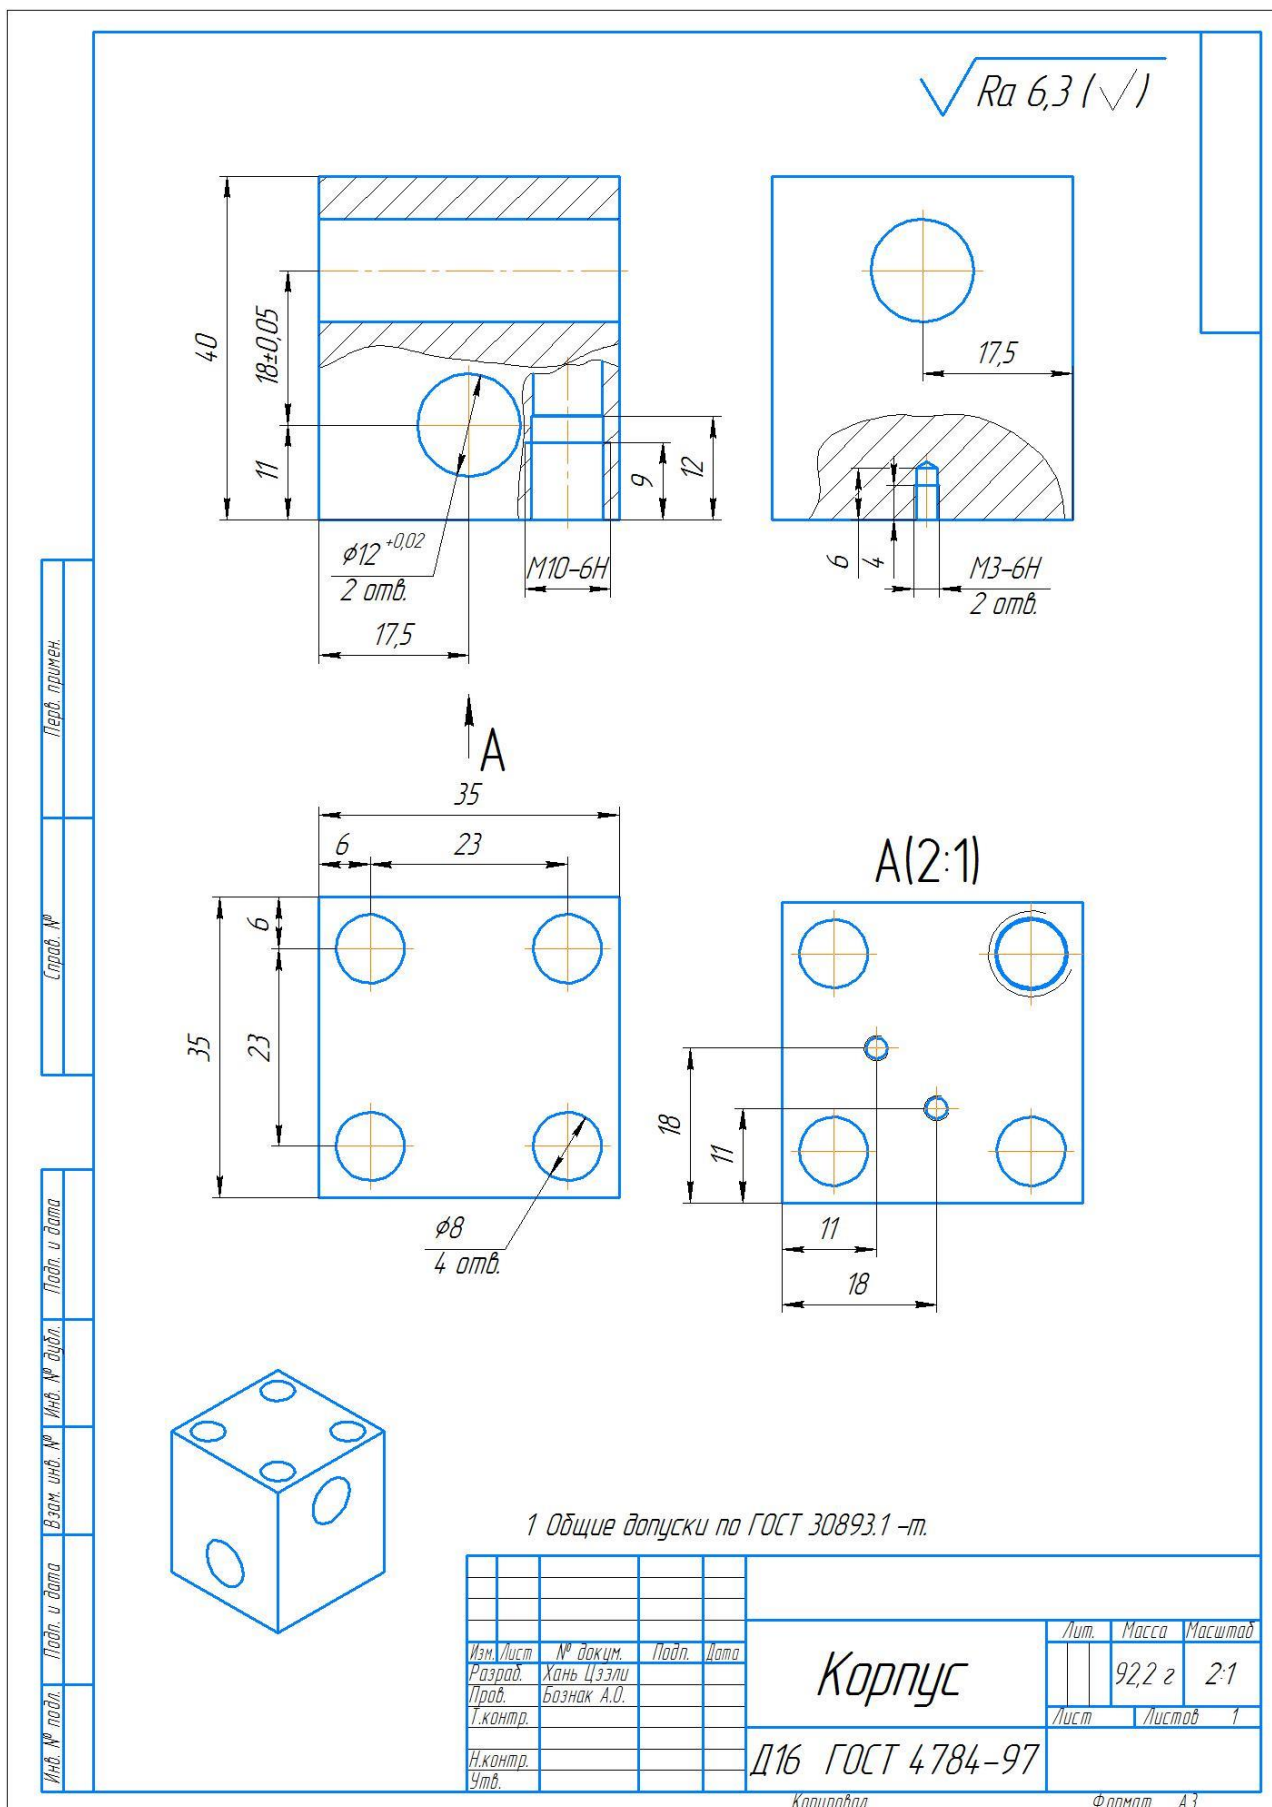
Чертеж детали «Корпус»
